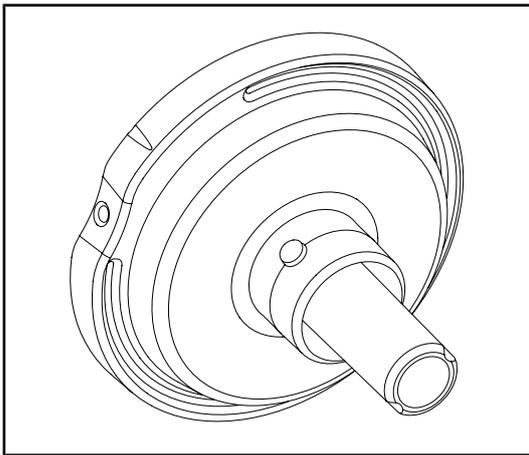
Держатель стерилизуемой рукоятки STG HLX
